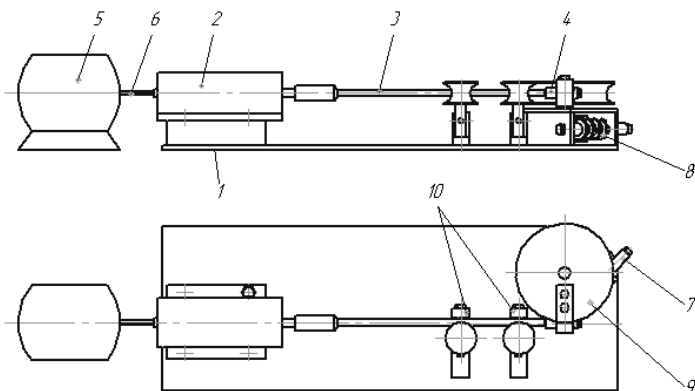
Схема установки для гибки мелкогабаритных труб
